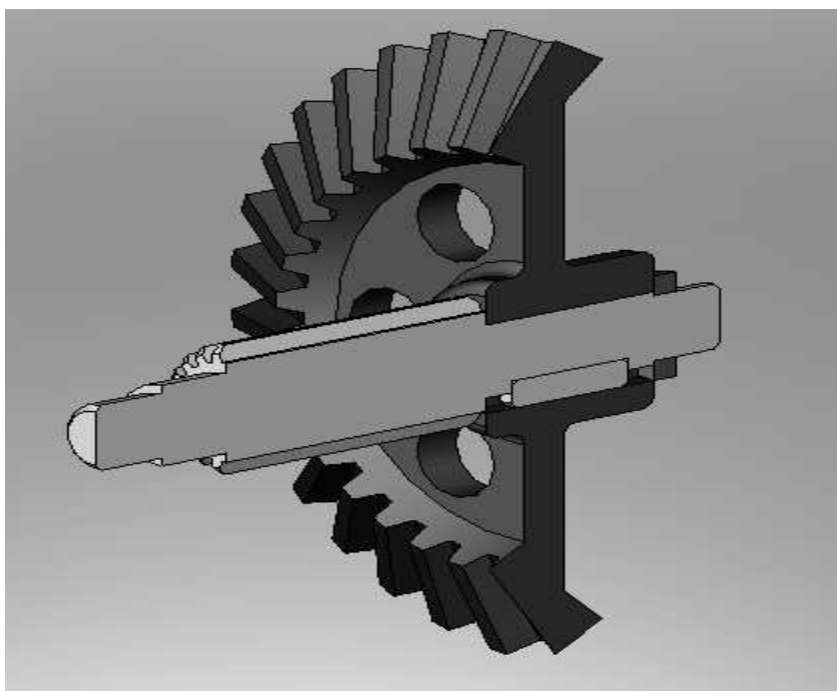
CAD-модель конструкции узла вала с коническим колесом
